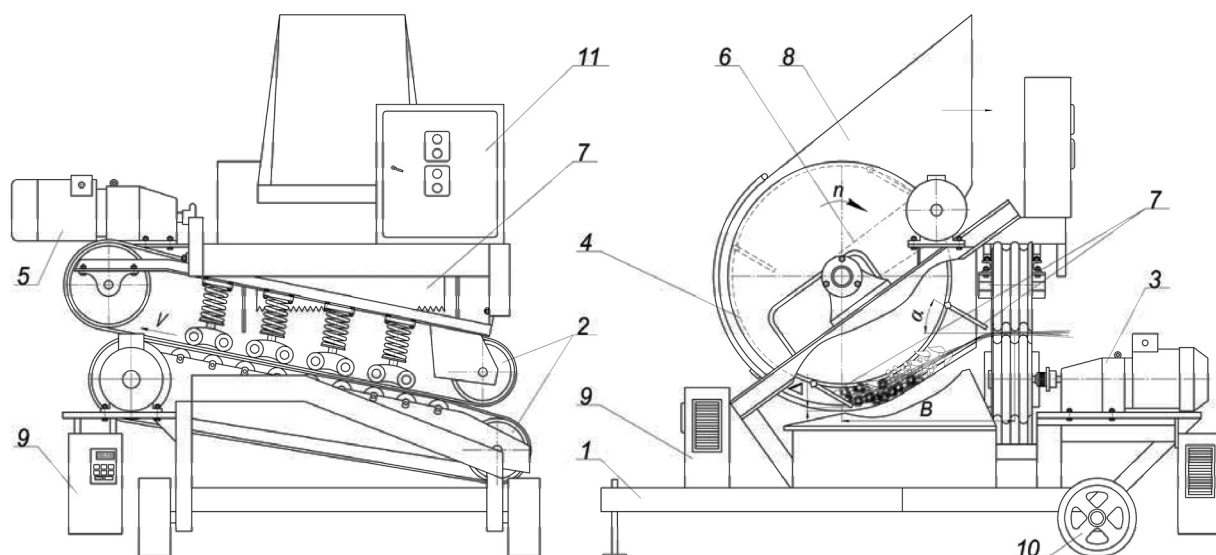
Схема лабораторной установки: 1 – рама; 2 – зажимной транспортер; 3, 5 – мотор-редуктор; 4 – барабан; 6 – цепная передача; 7 – эластичные гребенки; 8 – кожух; 9 – преобразователь частоты; 10 – колеса; 11 – пульт управления;  $\alpha$  – угол установки гребенки относительно плоскости зажимного транспортера;  $\Delta$  – зазор между гребенкой и подбарабаньем;  $n$  – частота вращения барабана;  $B$  – смещение ленты льна
